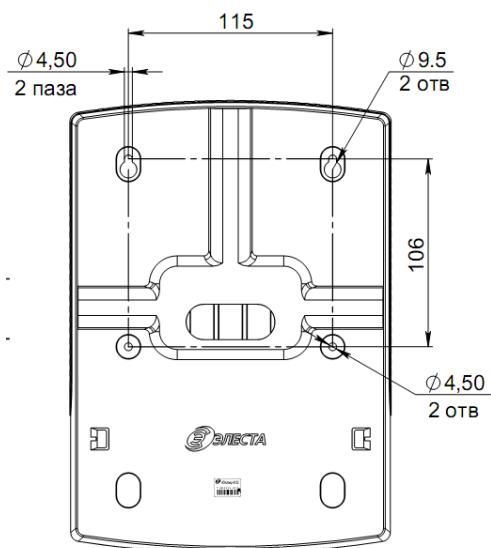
Габаритные и установочные размеры прибора Юпитер - 2029
